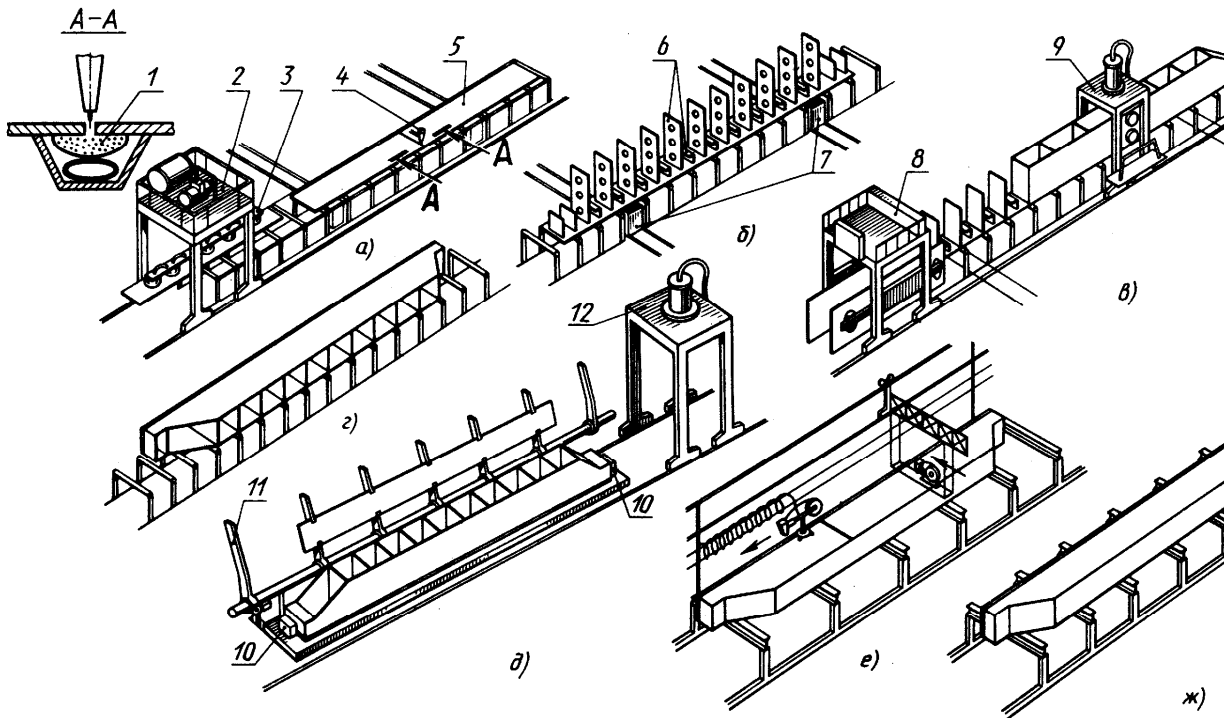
Участки поточной линии сборки и сварки главной балки
